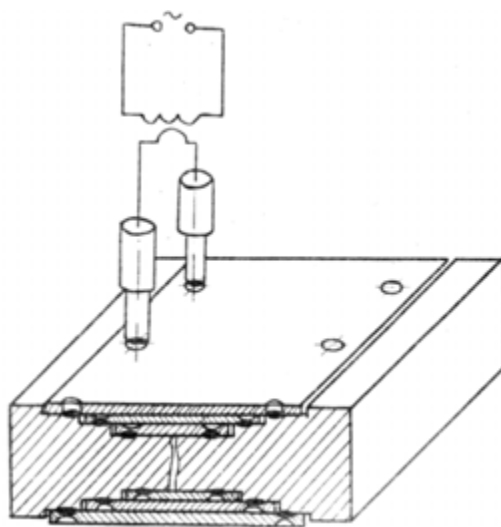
Схема реалізації клеєзварювального з'єднання (приварювання пластини до корпусної деталі)
